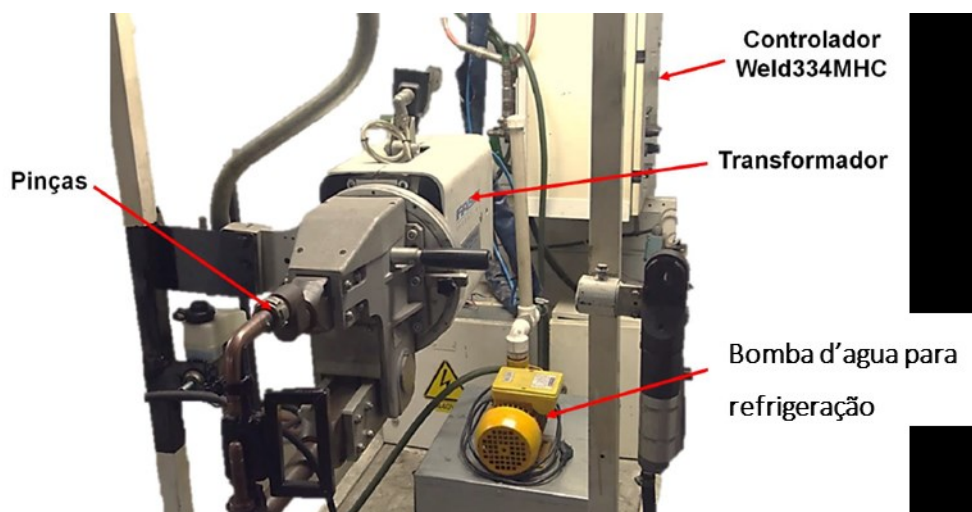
Máquina de soldagem a ponto por resistência elétrica (SOUSA, 2018)
